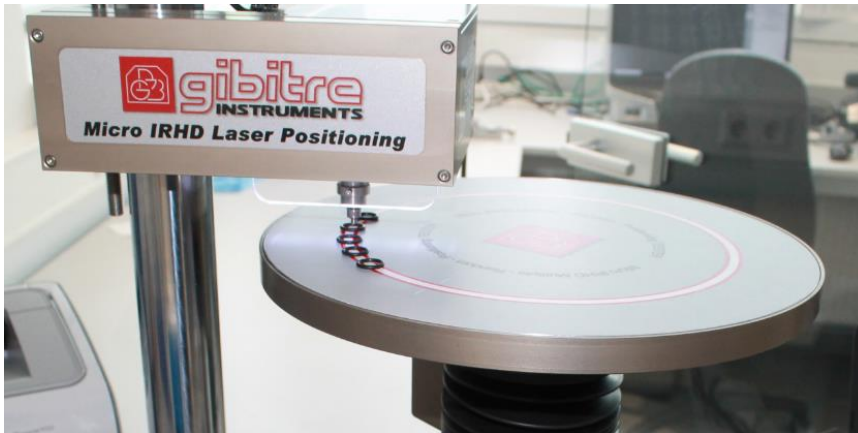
Der Drehteller wird manuell bestückt. Das IRHD,M-Prüfgerät fährt die O-Ringe automatisch an, um deren Härte zu prüfen (Foto: O-Ring Prüflabor Richter GmbH)
